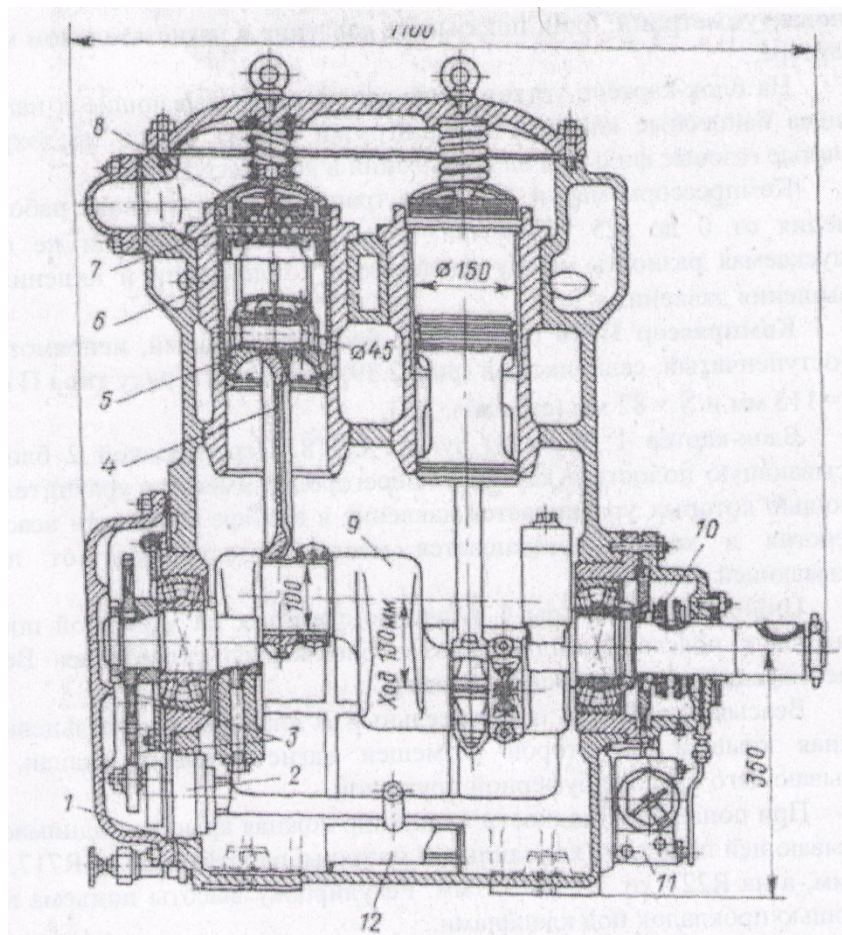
Одноступенчатый, прямоточный, U-образный базовый компрессор АУ-200: 1- блок картер; 2-шестеренный масляный насос; 3-привод насоса; 4-шатун;5-поршень;6-цилиндрическая гильза;7-всасывающий клапан;8-ложная крышка;9-коленчатый вал; 10- сальник; 11-щелевой масляный фильтр;12-заборный масляный фильтр.
